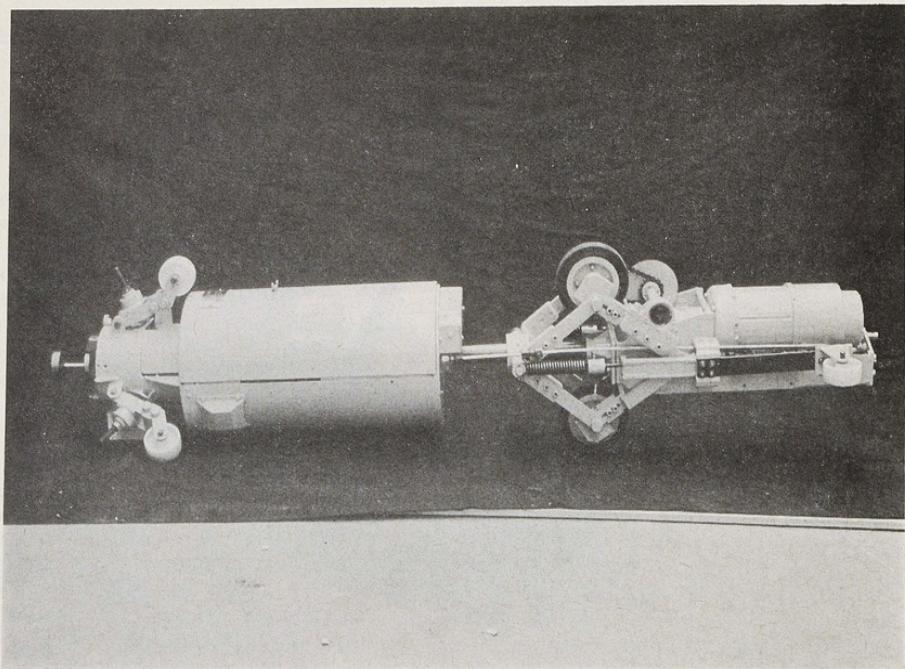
Pistolet portable pour soudage par faisceau d'électrons de tubes sur plaque tubulaire.
